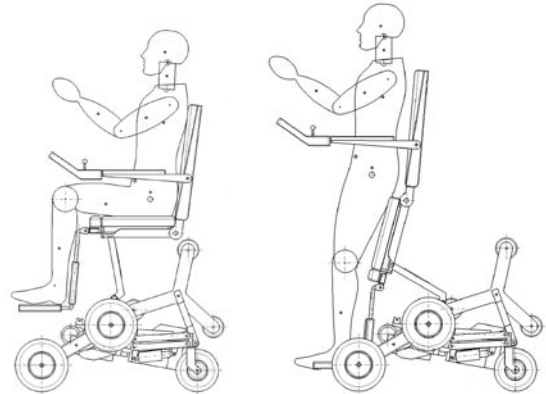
& 4 Anheben oder Aufrichten des Insassen für therapeutische Zwecke oder Komfortbelange
